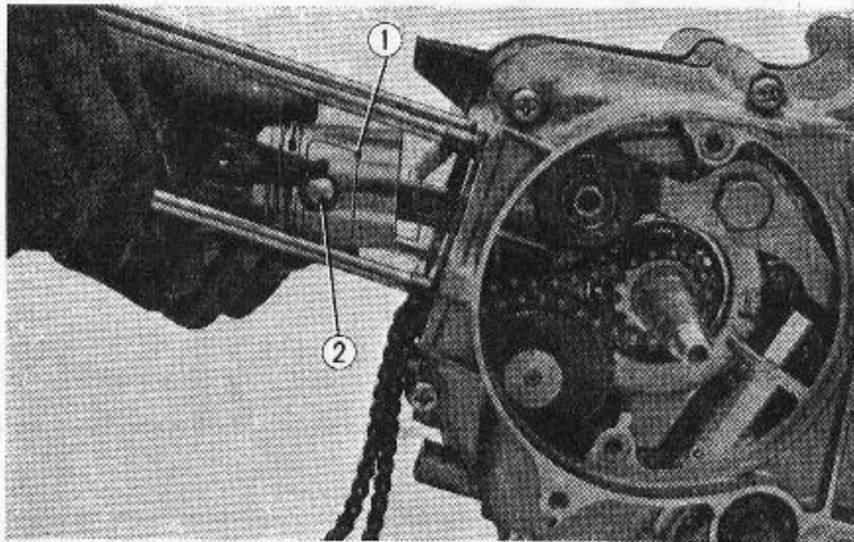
Kolbenbolzensicherungsring entfernen
